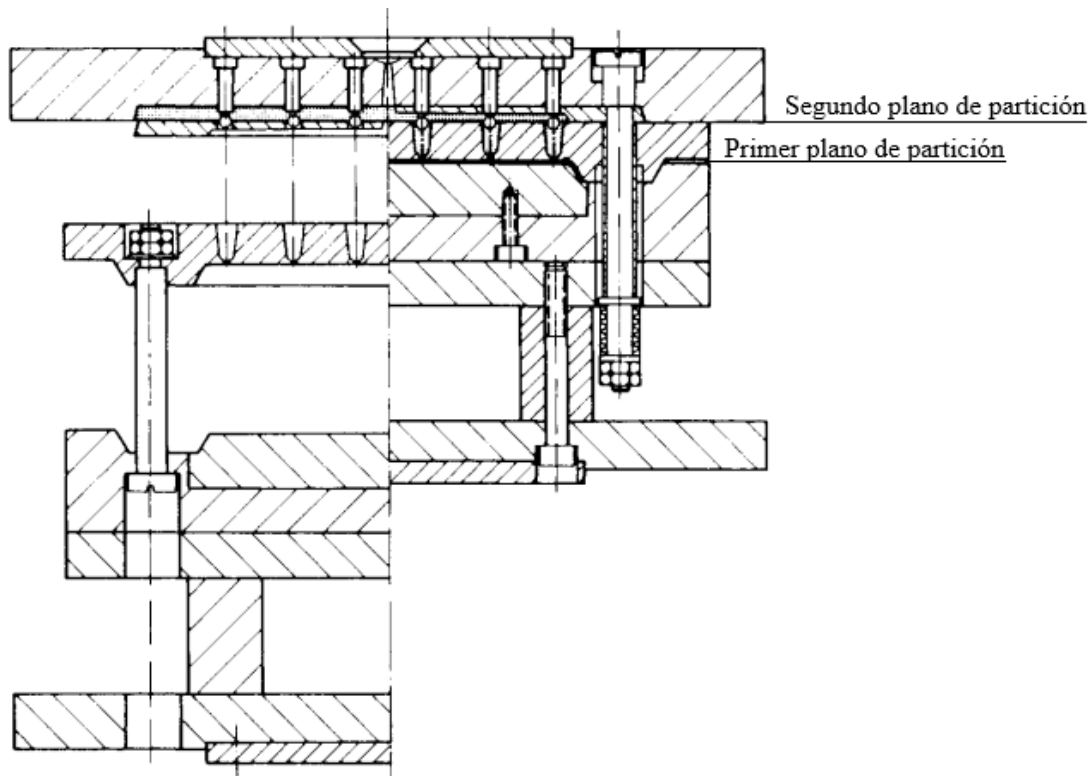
Molde de tres placas. Izquierda: abierto. Derecha: cerrado. Fuente: How to make injection molds [7].
